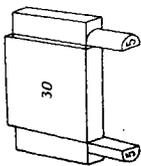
Meßschnäbel für Lochmessung mittels Endmaßen.
